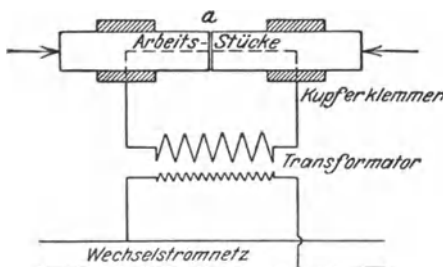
Schema der elektrischen Stumpfschweißung.
